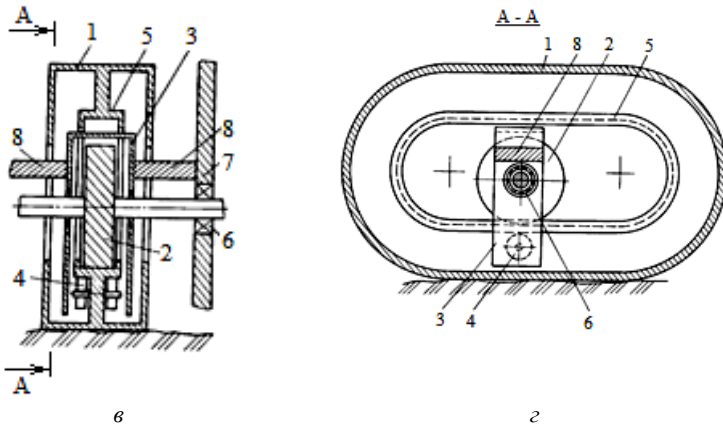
Колісно-крокуючий рушій транспортного засобу з коченням ведучого колеса по внутрішньому (а, б), зовнішньому (в, г) контуру порожнистого колеса: 1 – порожнистий корпус; 2 – колесо з віссю; 3 – П-подібний кронштейн; 4 – притискні ролики; 5 – стінка; 6 – підшипник; 7 – борт транспорту; 8 – фіксатор П-подібного кронштейна
